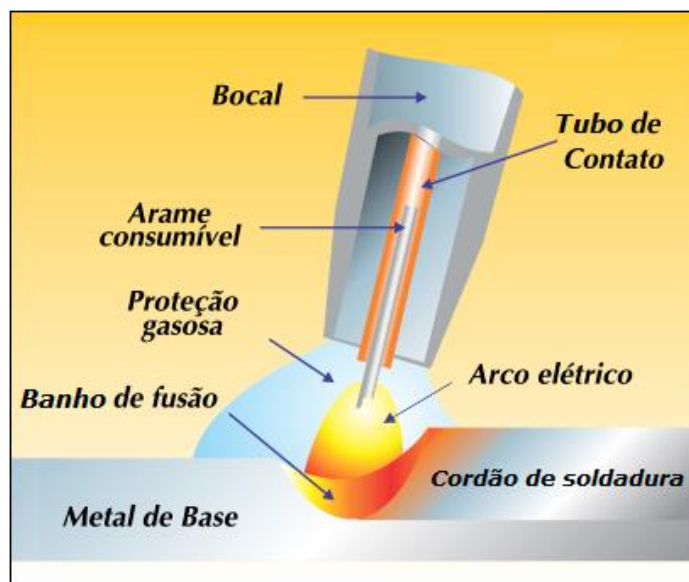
Ilustração do processo de Soldadura MIG/MAG [Adaptado de (Gastolin, 2017)].
